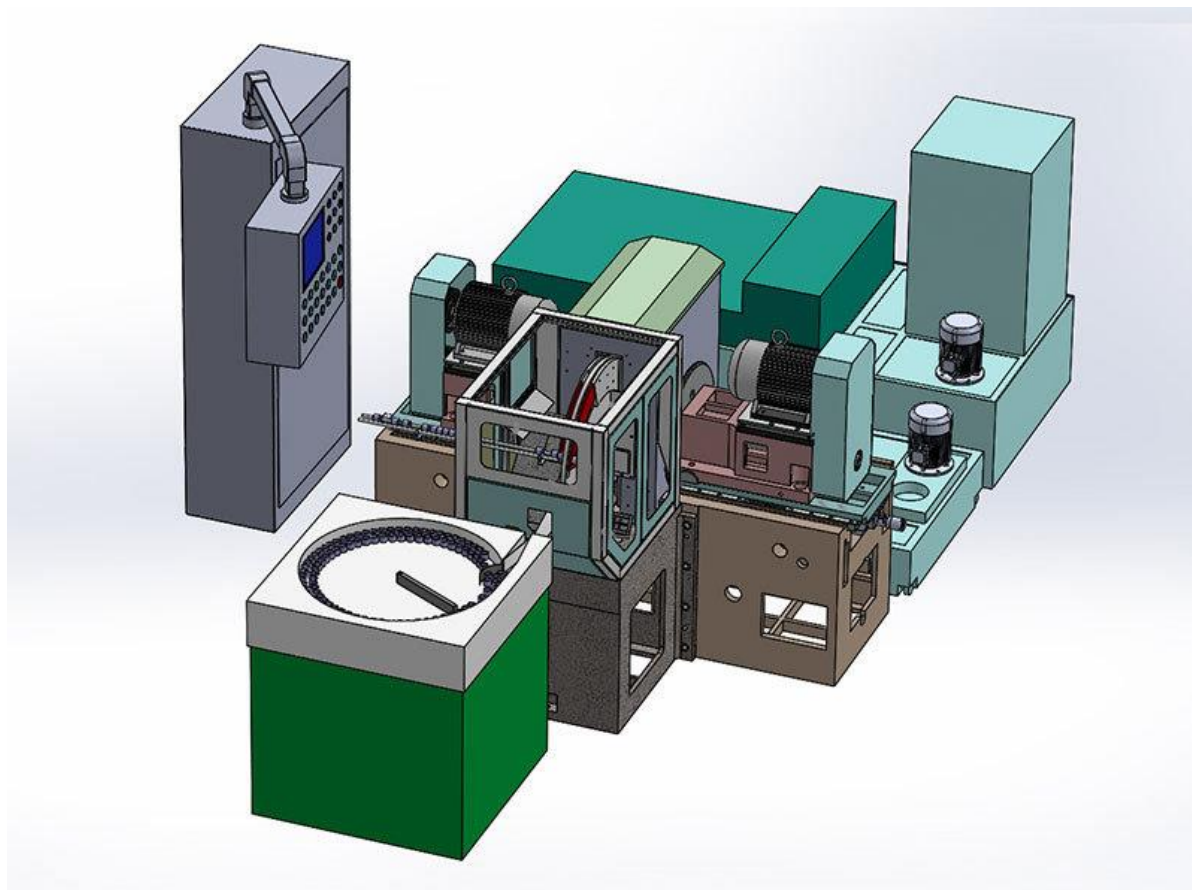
Двосторонній горизонтальний торцешліфувальний верстат з ЧПК мод. DRG-585 фірми Rushan Shuangxing Machine Tool Manufacturing Co., Ltd SATURN (Китай)
